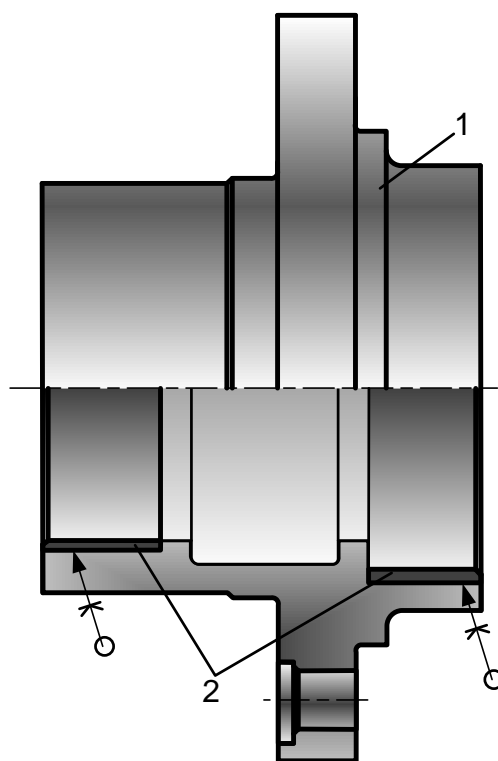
Схема восстановления гнезд под подшипник постановкой дополнительных деталей:
